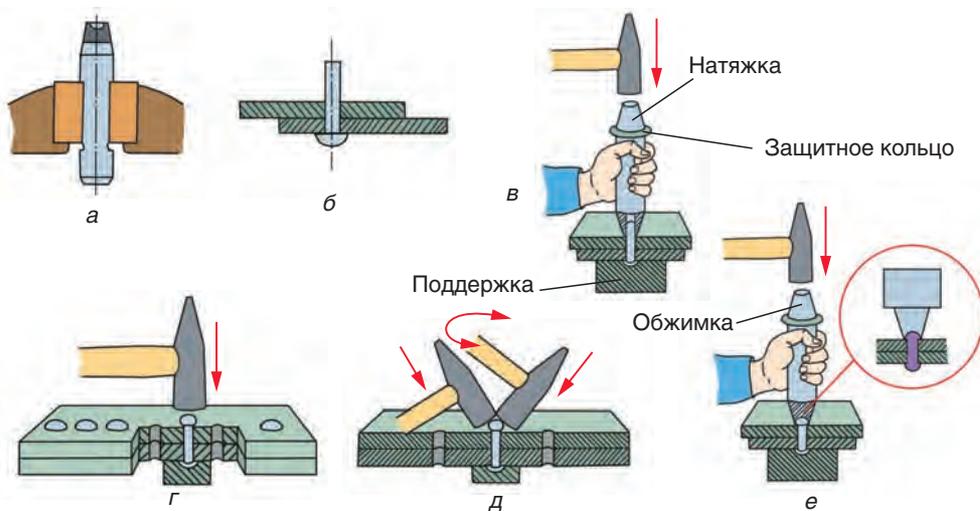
Приемы выполнения заклепочного соединения заклепкой с полукруглой головкой
